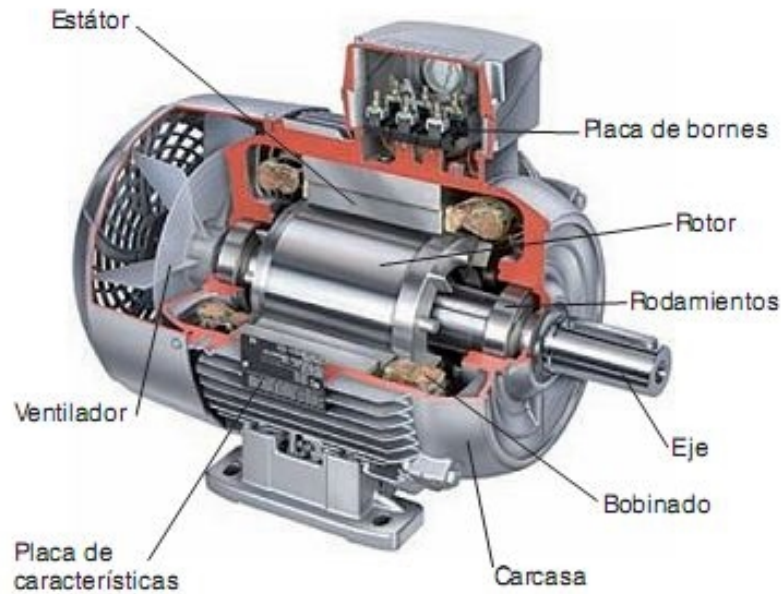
Vista de corte de un motor de inducción Fuente: [45]
